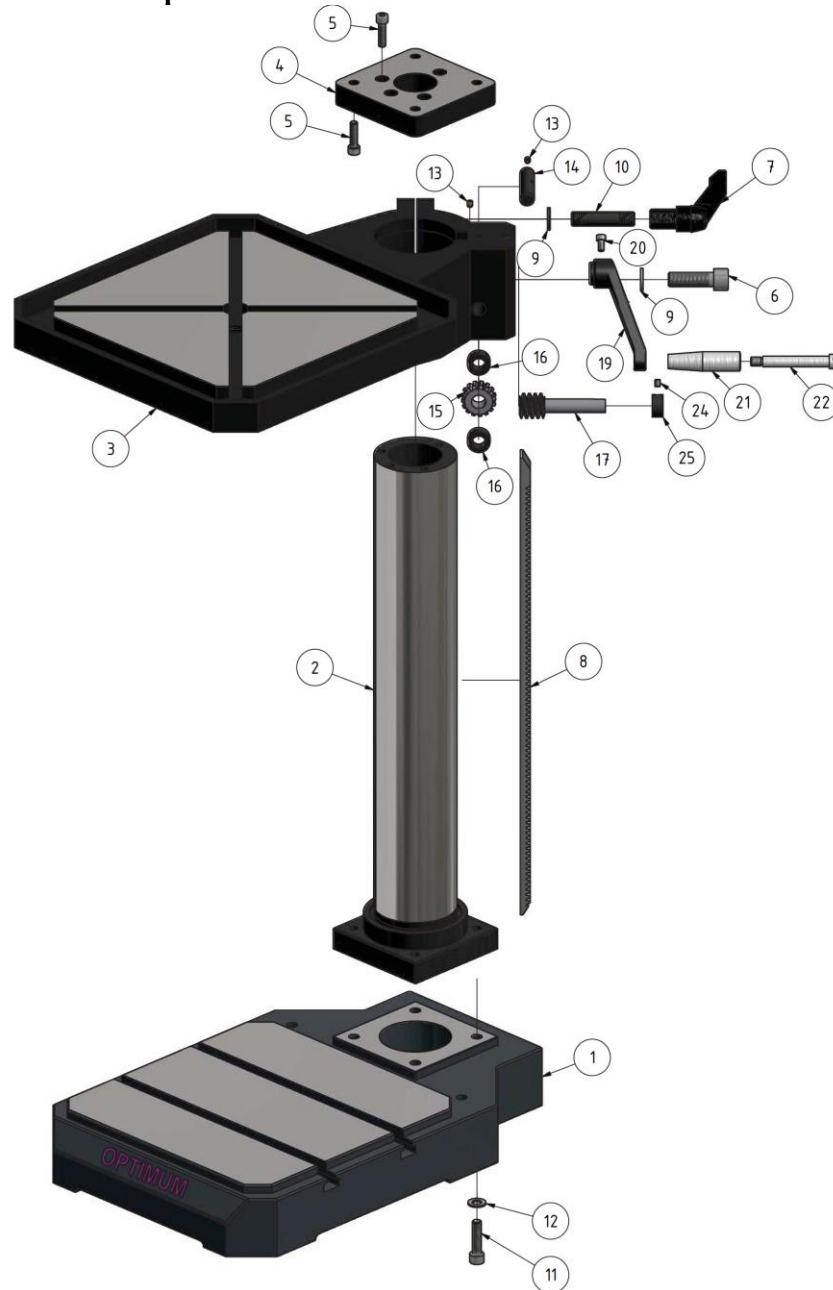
Стол сверлильного станка – DH 26 GT
